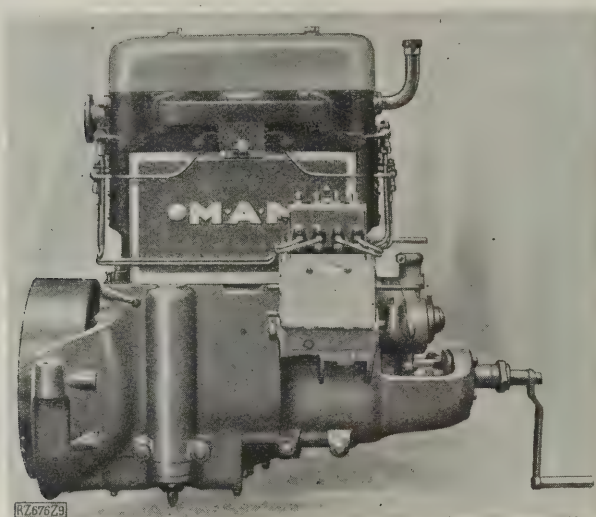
Ansicht des Fahrzeug-Dieselmotors der MAN.
